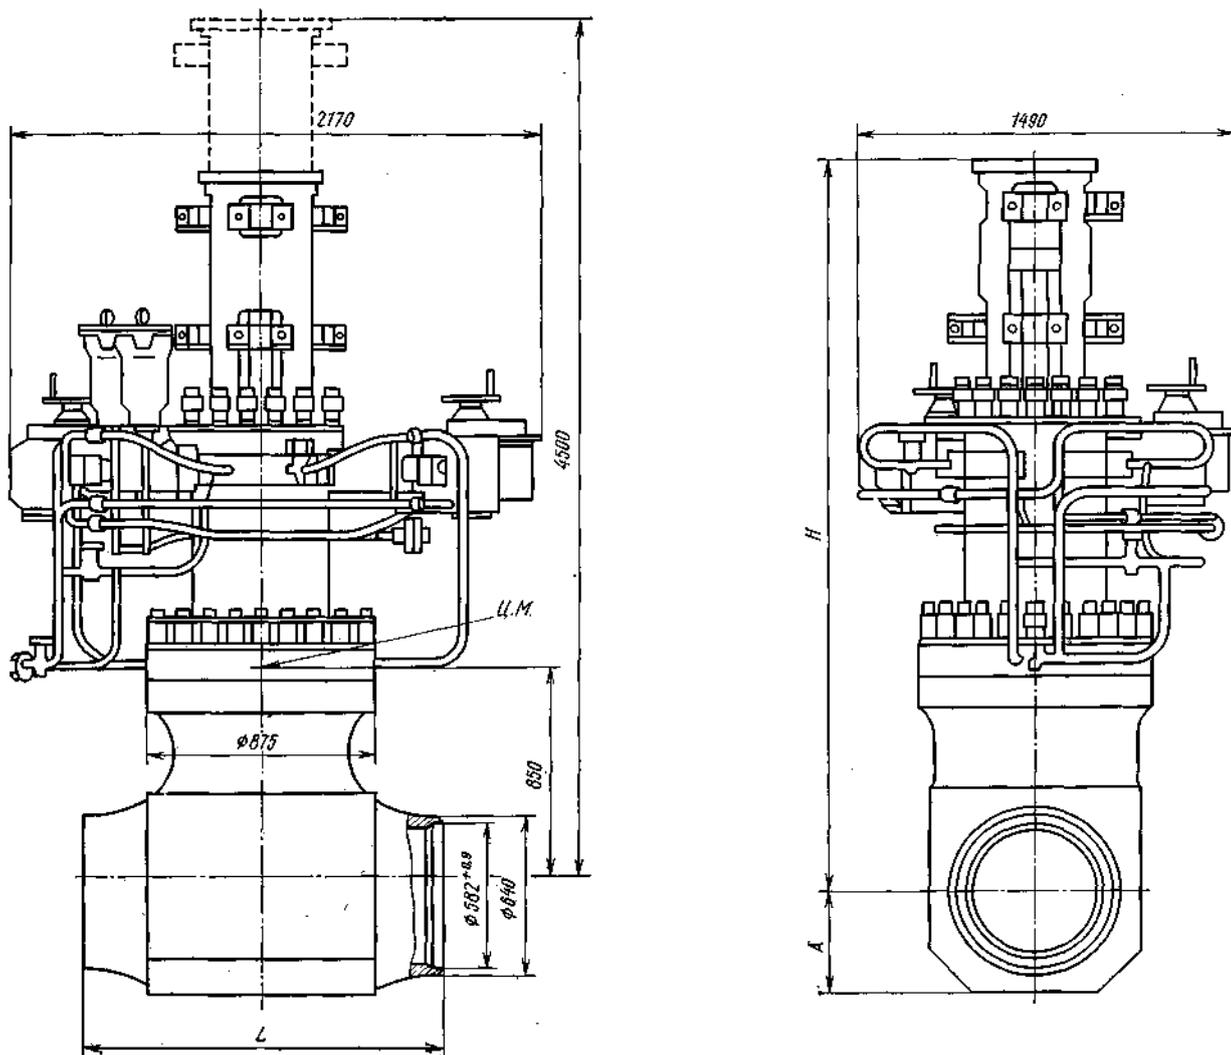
Задвижка быстродействующая D_y 600 для II контура АЭС с реактором ВВЭР-1000
